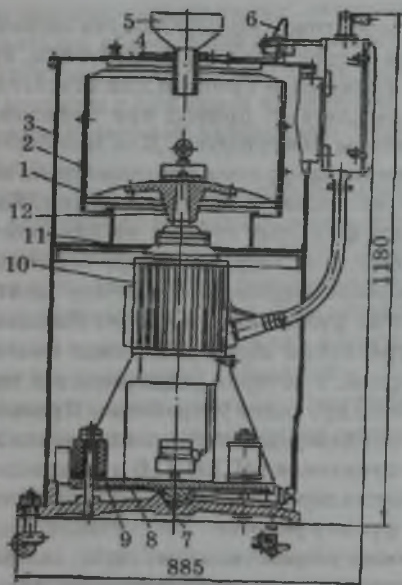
Опорная фильтрующая центрифуга ОЦС:
